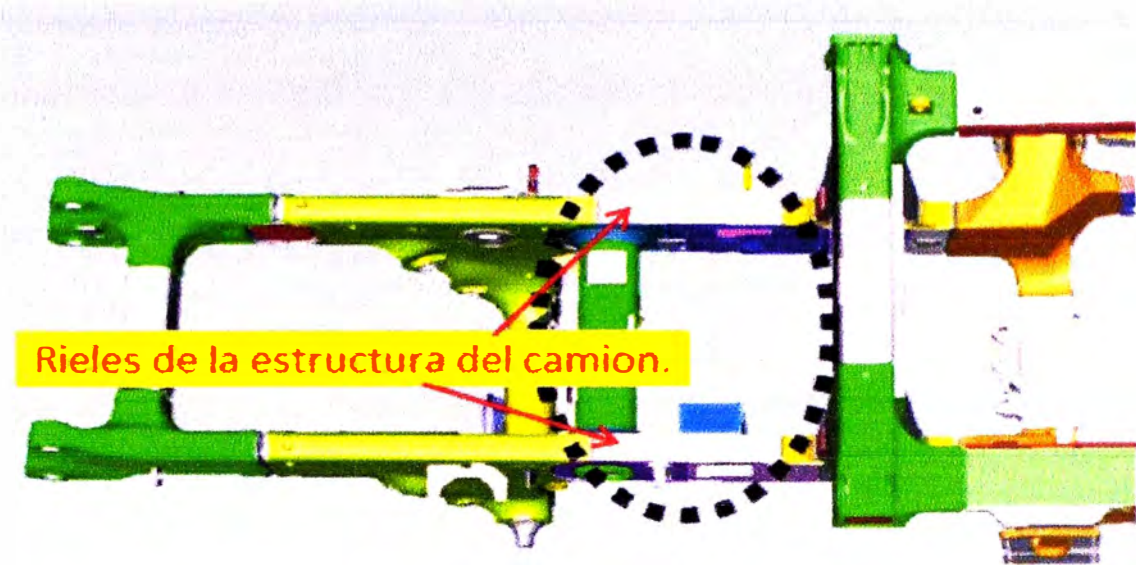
Ubicación de los rieles de la estructura del camión.
